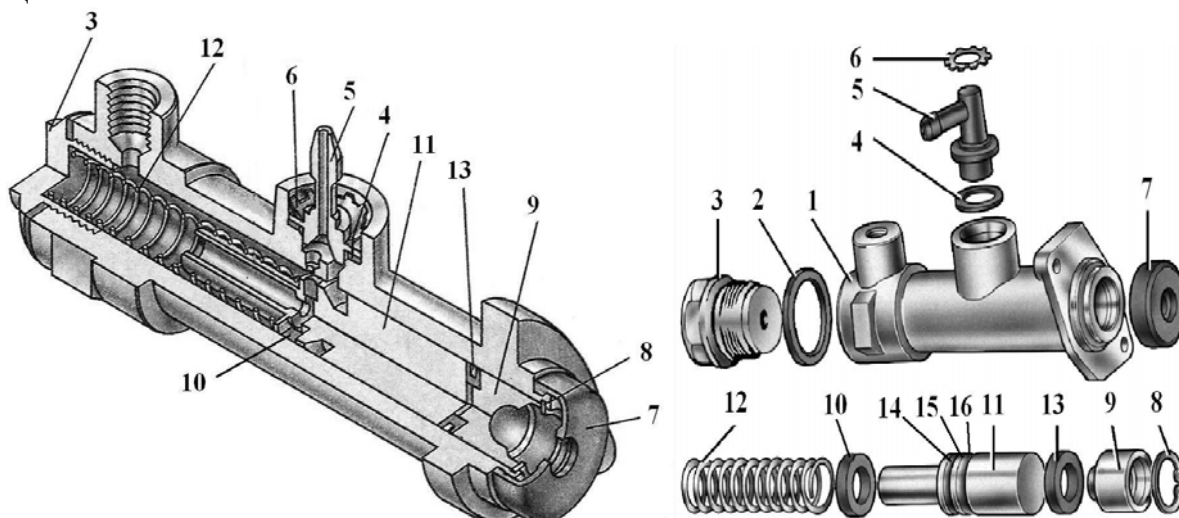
Главный цилиндр гидропривода выключения сцепления автомобилей ВАЗ:
